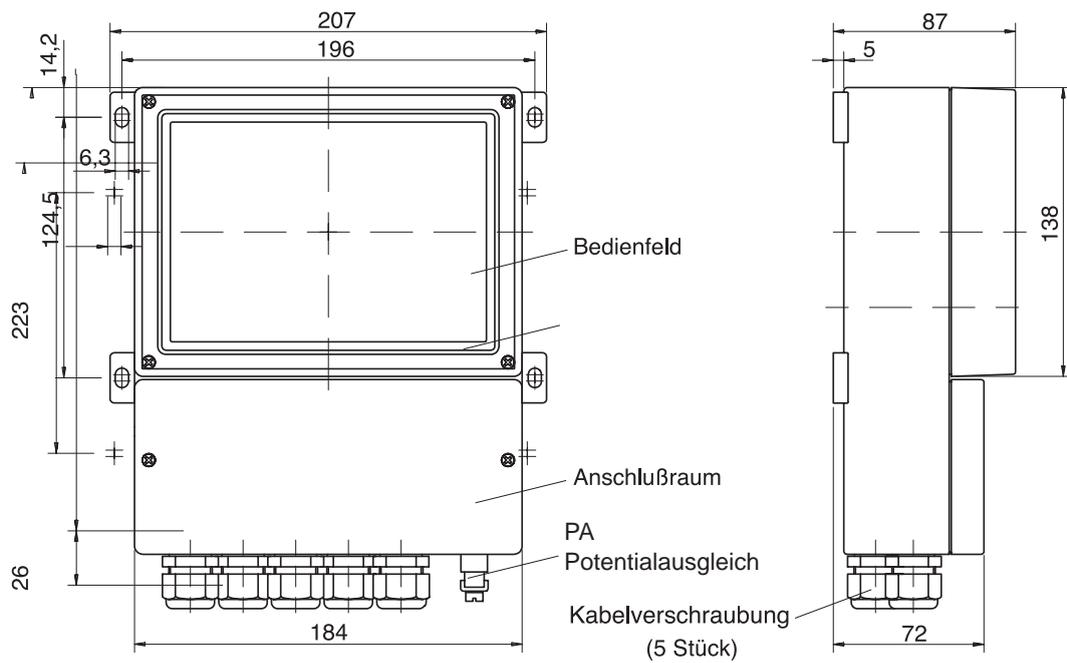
Maßzeichnung O₂-Transmitter 4220X
